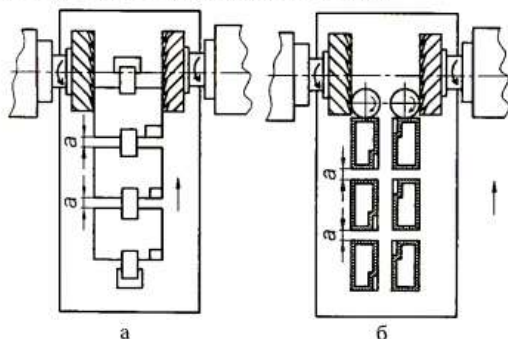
Групова установка деталей на повздожно-фрезерному верстаті: а – установка в один ряд; б – установка в два ряди
